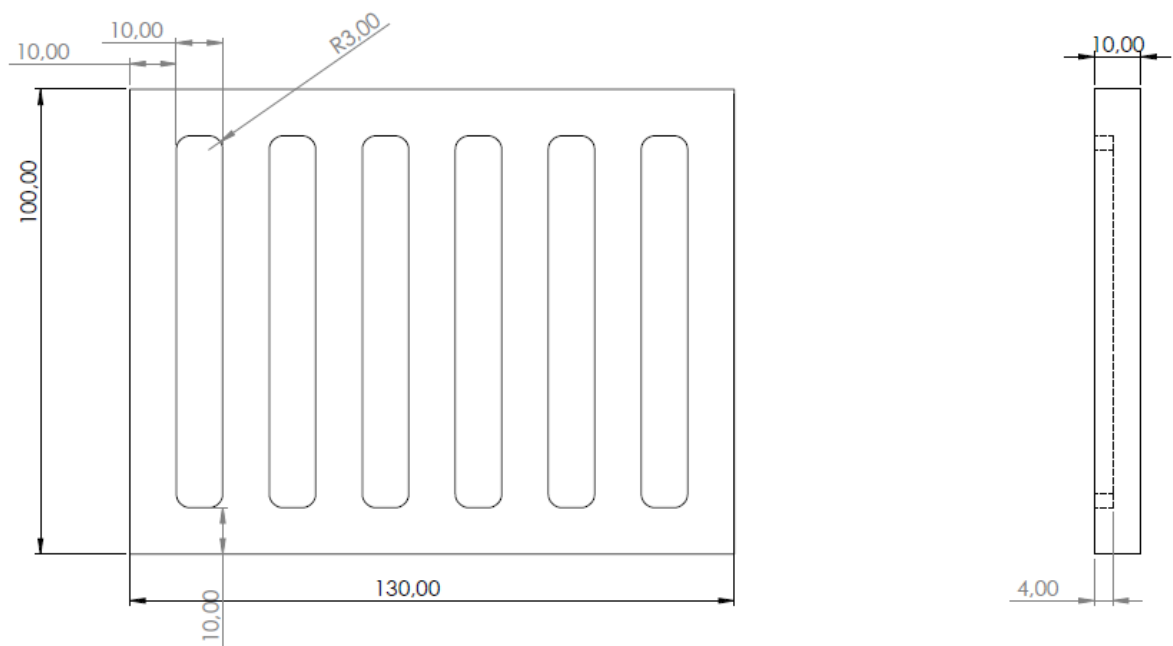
Molde para ensaio de flexão segundo norma ISO 178 [32] com dimensões em mm.
